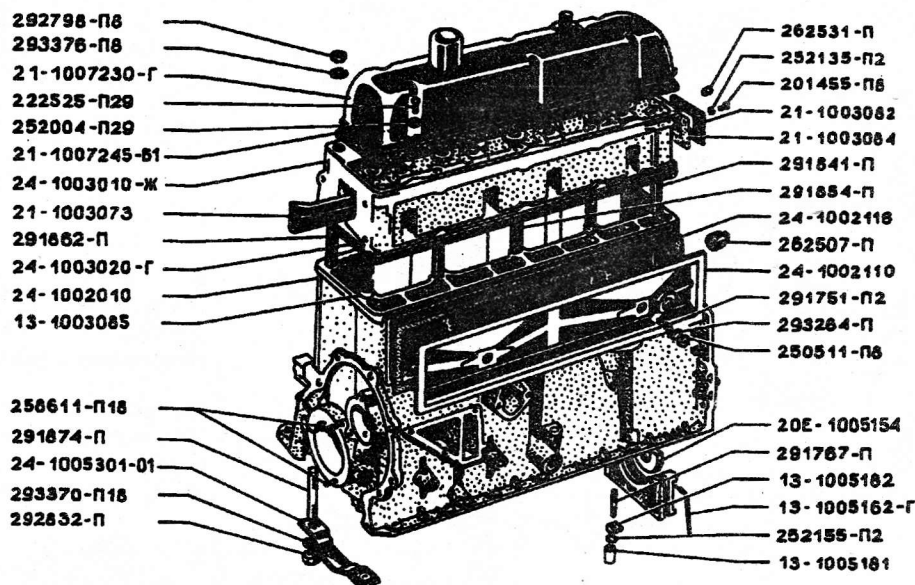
Блок цилиндров двигателя; головка цилиндров двигателя
